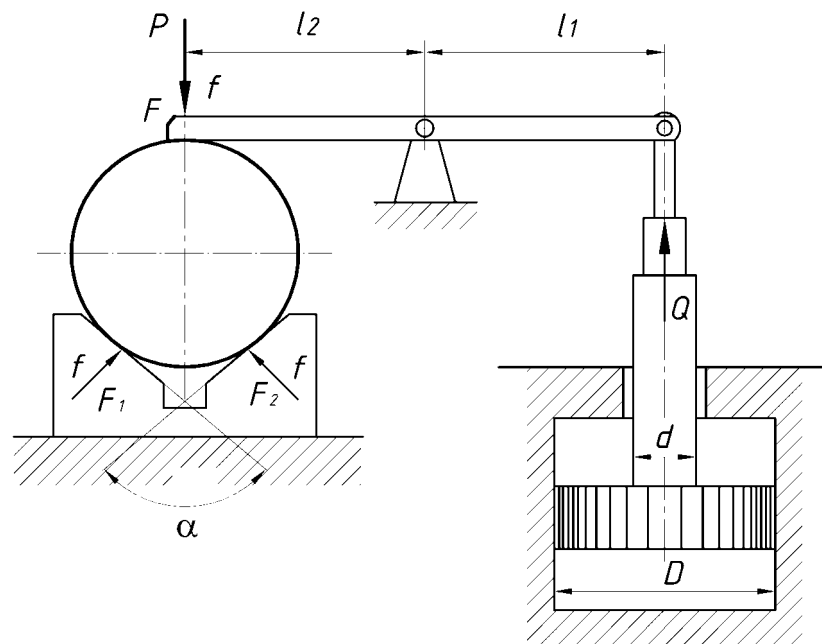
Схема дії сил в пристрої для фрезерування торця
